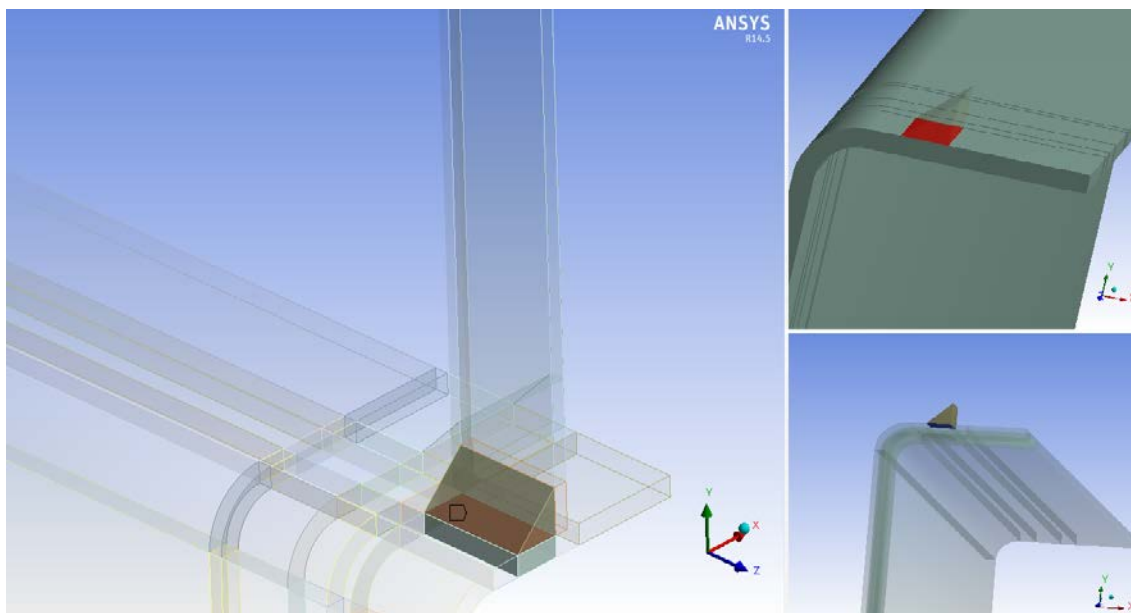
Modelo 2. Contactos: Soldadura sobre cordón
